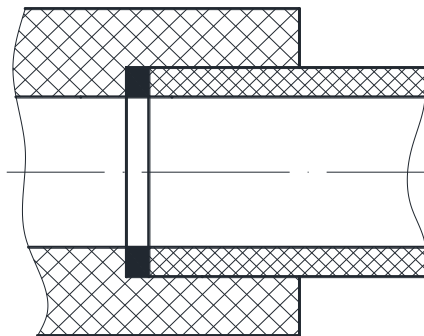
Конструктивные элементы шва сварного соединения (швы НС3 и НС4)
